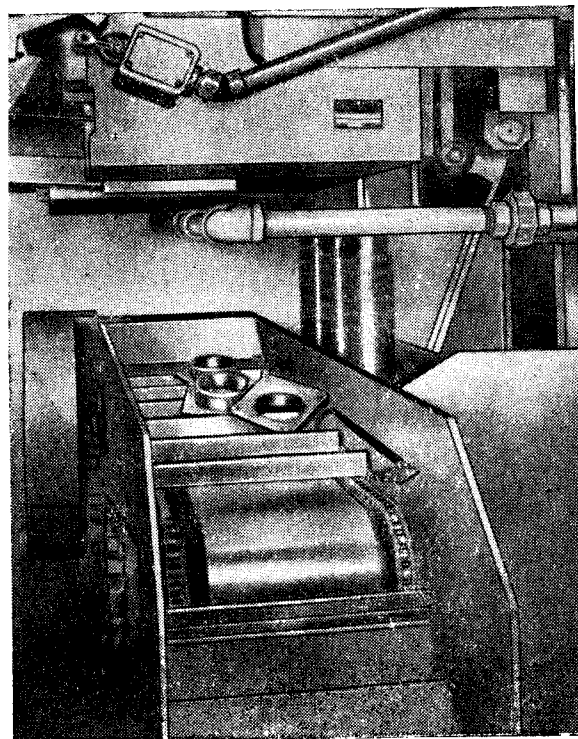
Конвейер для удаления обработанных деталей с вертикально-протяжного станка
